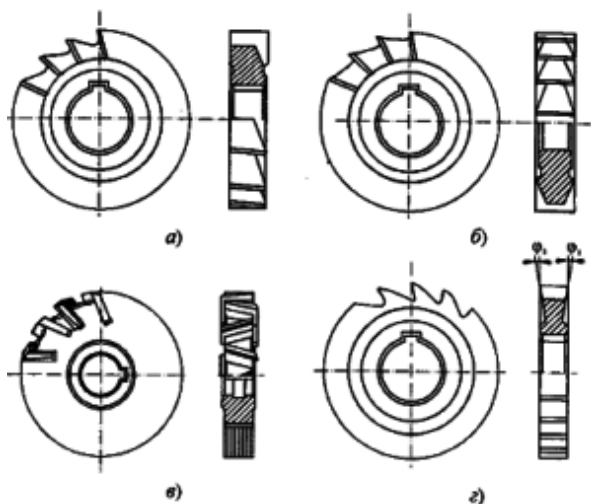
Виды дисковых фрез: а – двухсторонние; б – трехсторонние; в – трехсторонние с разнонаправленными зубьями; г – пазовые; — угол поднутрения
